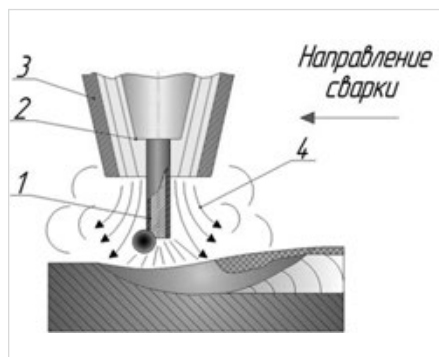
Схема процесса сварки порошковой проволокой в защитном газе. 1 — проволока, 2 — токоподвод, 3 — сопло, 4 — защитный газ
